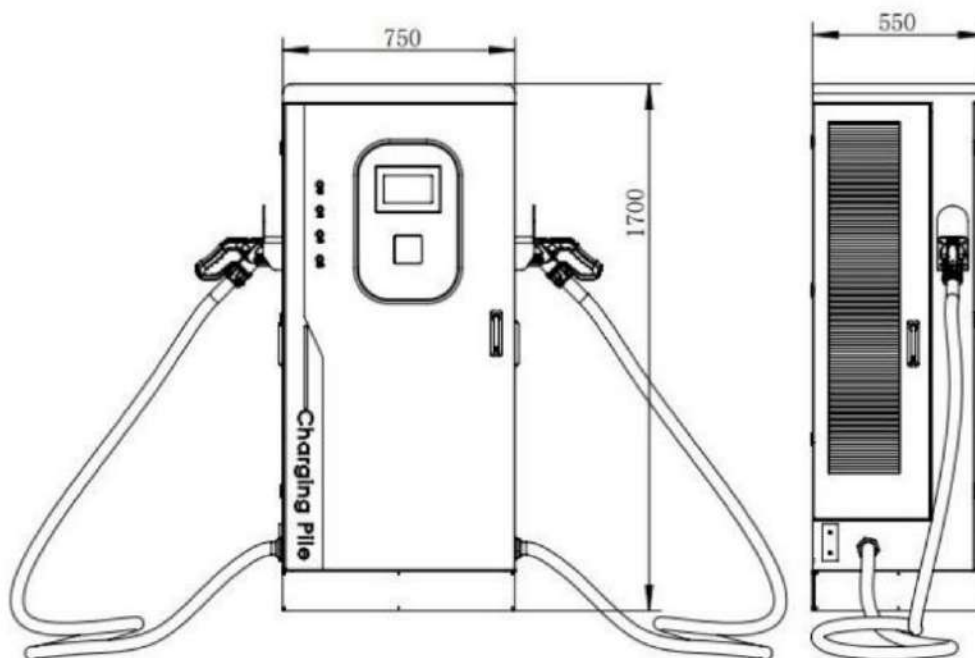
Dimensiones del equipo (MDDC-120kW/160kW)
